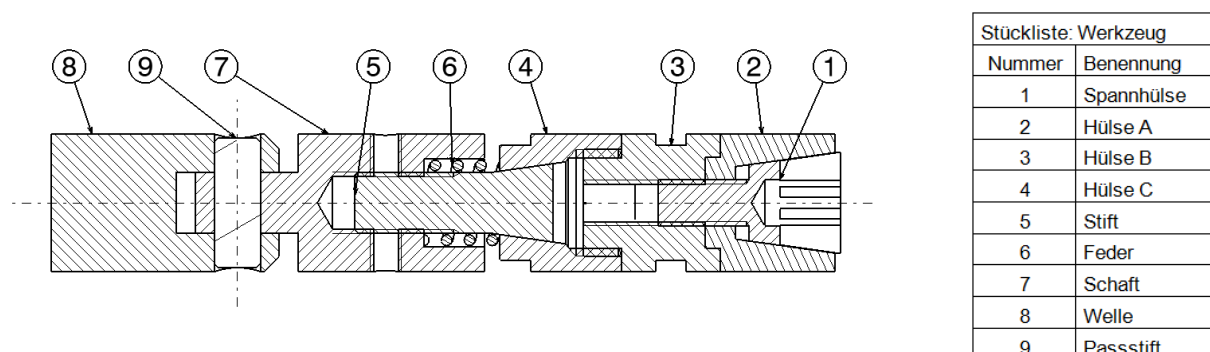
Aufbau des Werkzeuges mit Kugelfräser
